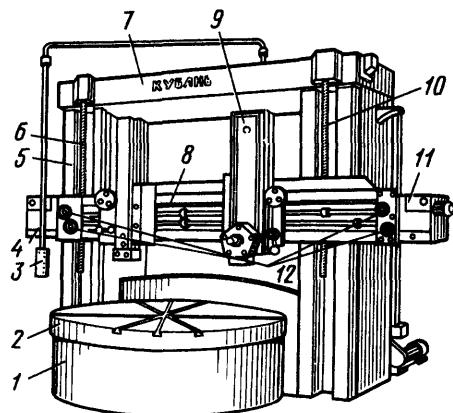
Двухстоечный токарно-карусельный станок модели 1525
